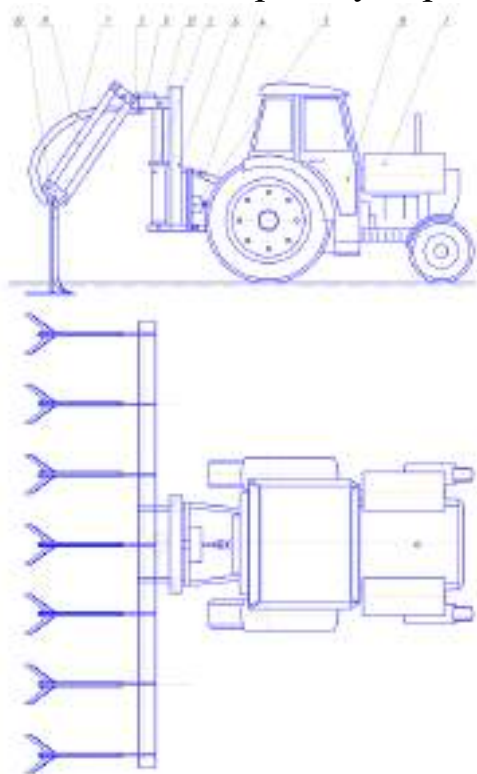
Схема широкозахватного агрегату: 1 – балони обприскувача; 2 – гідроциліндр; 3 – кріплення навіски; 4 – навіска; 5 – насос; 6 – рама культиватора; 7 – рукав; 8 – трактор; 9 – трубопровід; 10 – лапа культиватора; 11 – підвіска паралелограмна; 12 – рухома рама.
